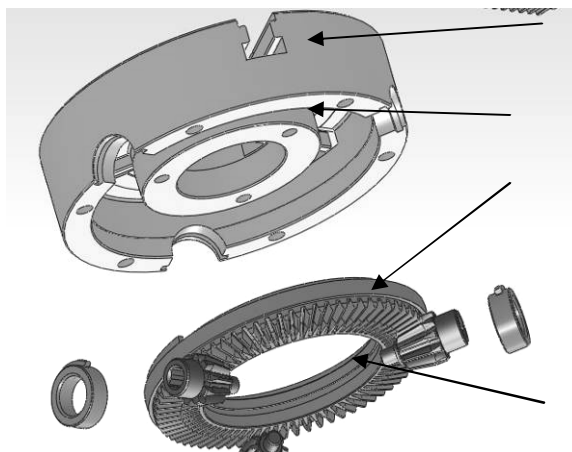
Поверхности токарного патрона с ротапринтным покрытием
